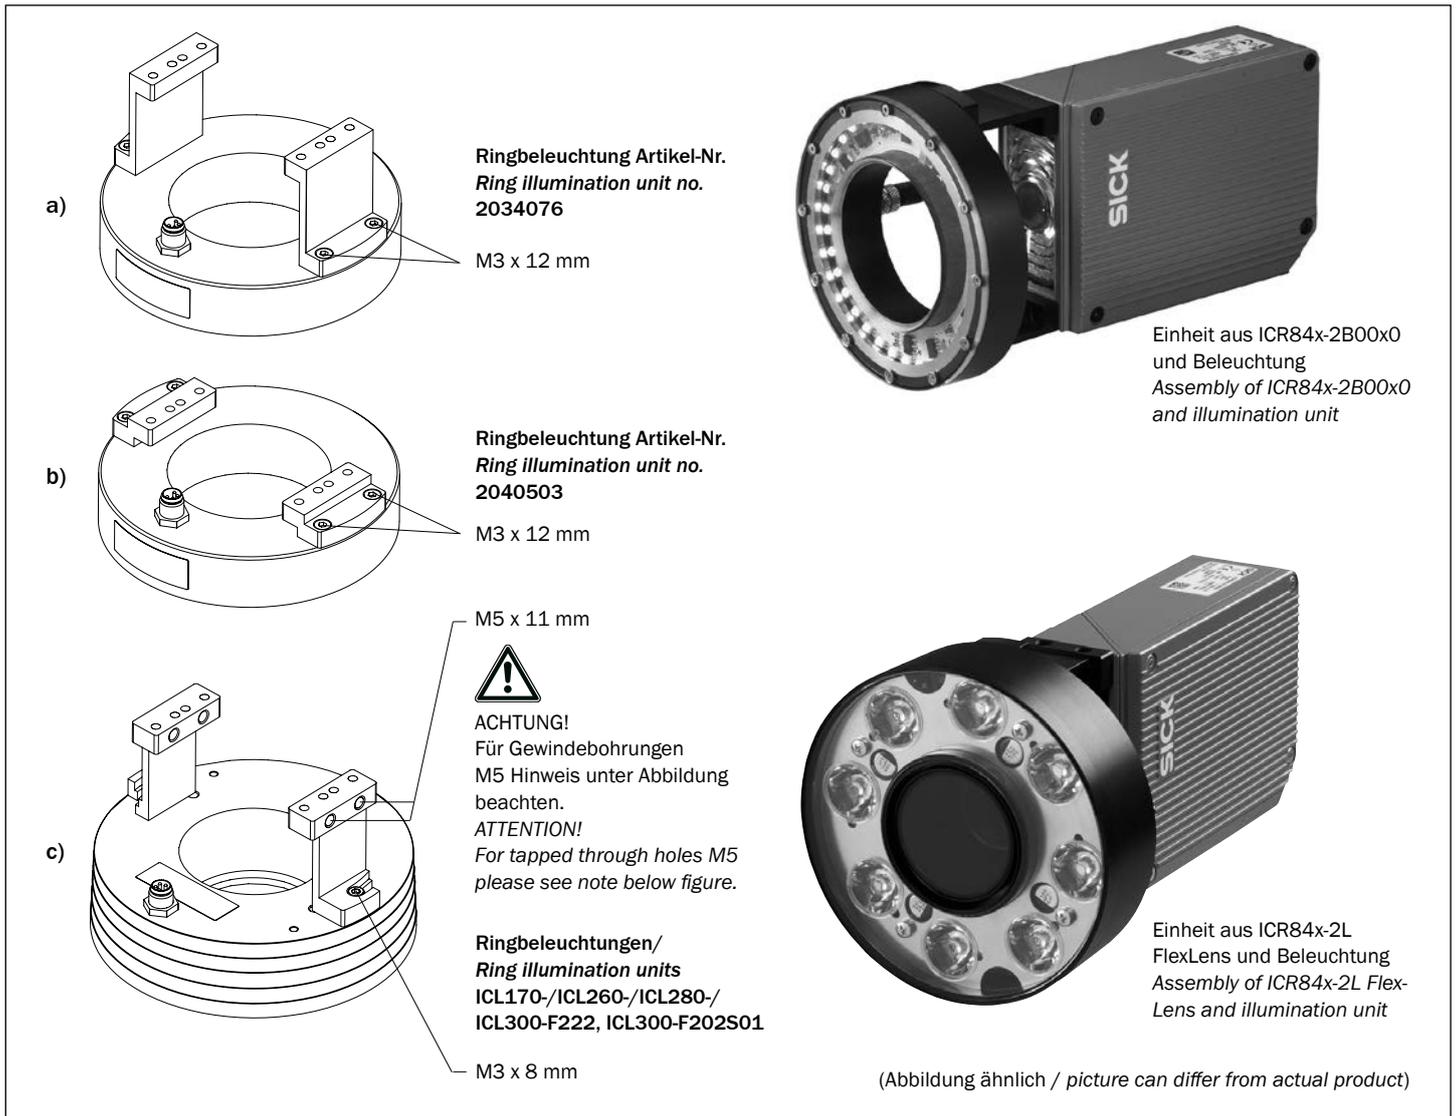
Montage der Befestigungswinkel an der Ringbeleuchtung / Fig. 4: Mounting the brackets on the ring illumination unit
